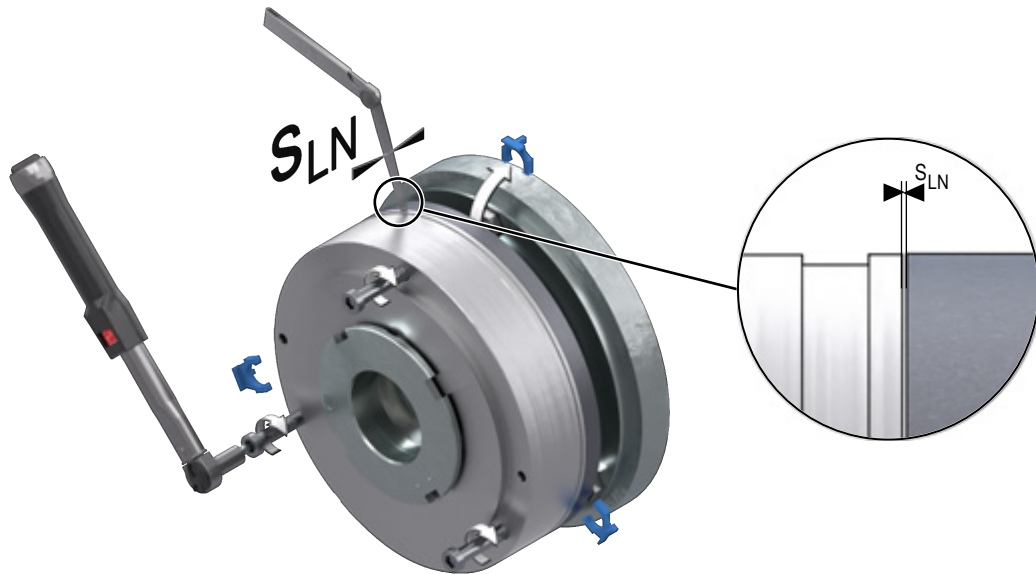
Anziehen der Schrauben mit Drehmomentschlüssel
